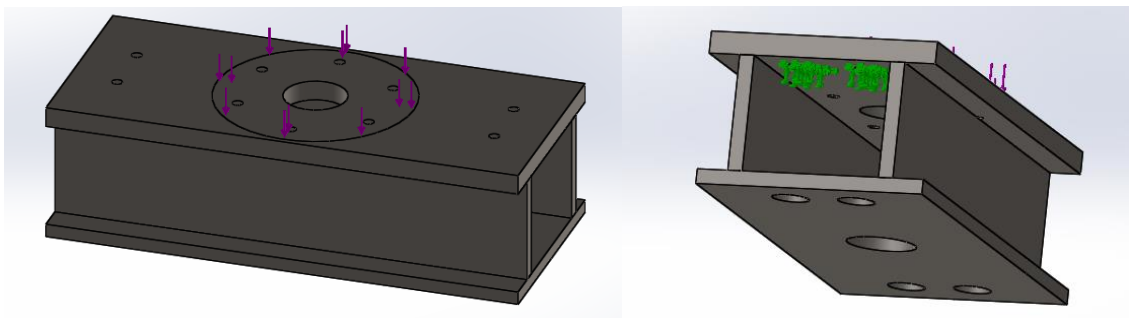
Ubicación de fuerza y geometrías fijas, simulación viga tipo cajón.
